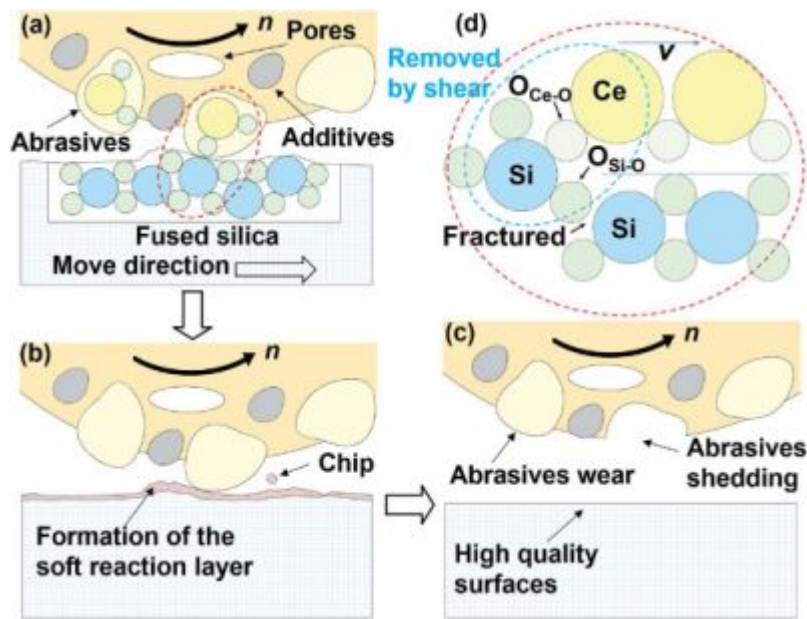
Механізм реакції видалення між зернами мікрошліфувальних інструментів і заготовкою: (а) реакція почалася, (б) шар пом'якшення був утворений і видалений з поверхні заготовки шар за шаром, (с) попередня стадія повторюється до отримання високоякісної поверхні, (д) збільшене зображення розриву та утворення хімічних зв'язків під час реакції [12]
